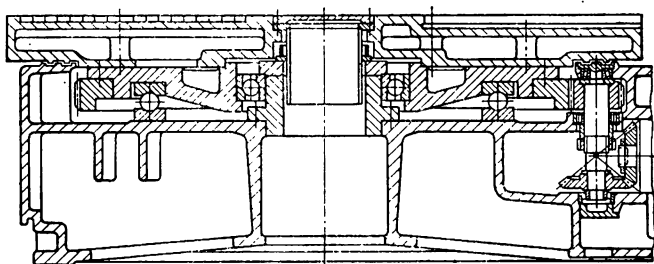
Схема стола на подшипниках качения с центрированием и прижимом планшайбы одним радиально-упорным шарикоподшипником
